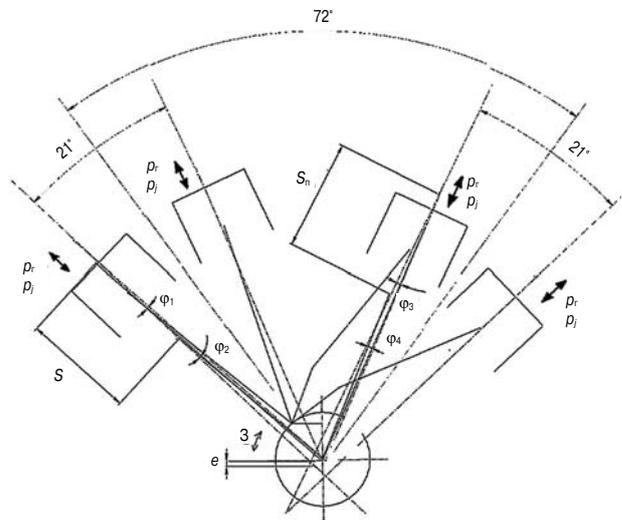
Кинематическая схема W-образного двигателя с прицепными шатунами:
